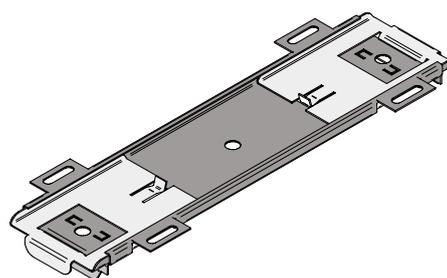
Élément d'assemblage ADRIATIC d-T-MD-4S, pour installation directement contre le plafond.
